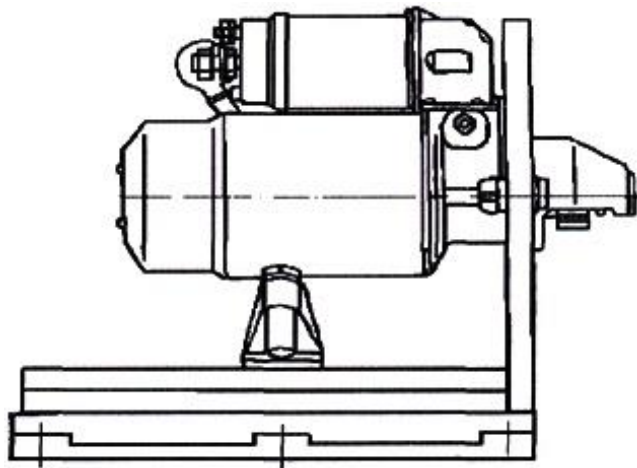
Установка стартера за фланец на столе нагрузочного устройства
